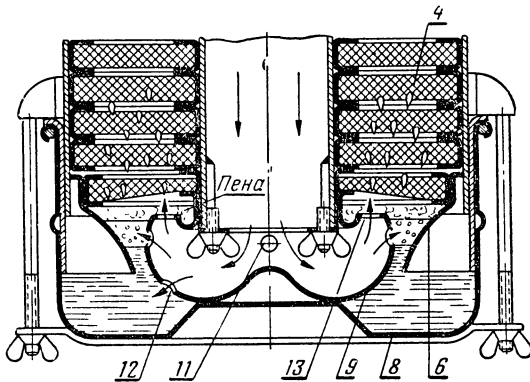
Схема движения воздуха в чашке и поддоне воздухоочистителя (обозначения позиций даны в подписи под рис. 61).
